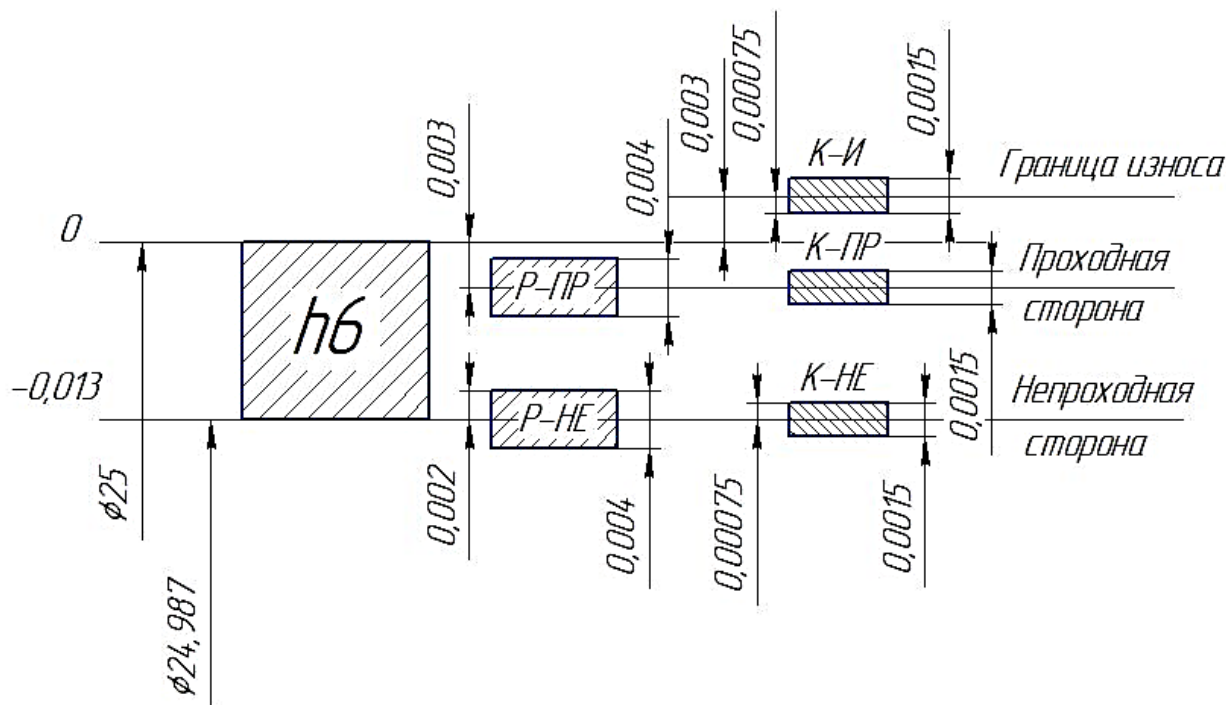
Схема полей допусков калибра-скобы для контроля деталей соединения $\phi 25h6$
